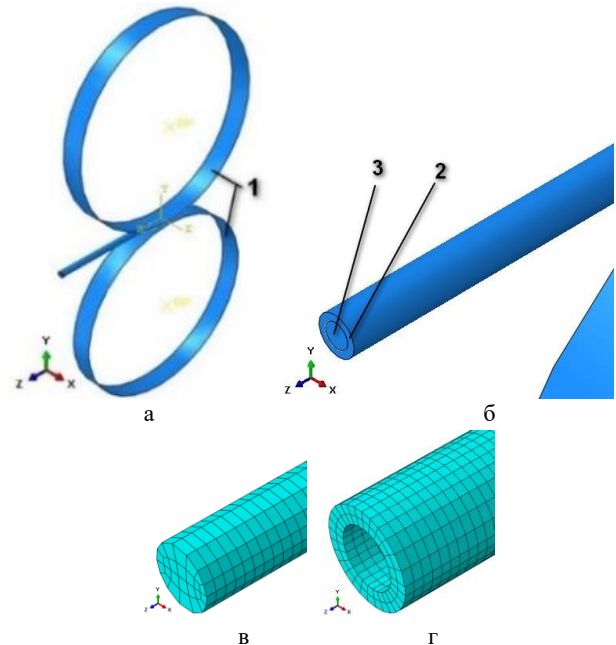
Конечно-элементная модель процесса плющения порошковой проволоки (1 – рабочие валки; 2 – металлическая оболочка; 3 – порошковый сердечник): а – расчетная схема; б – заготовка; в – конечно-элементная сетка порошкового сердечника; г – конечно-элементная сетка металлической оболочки
